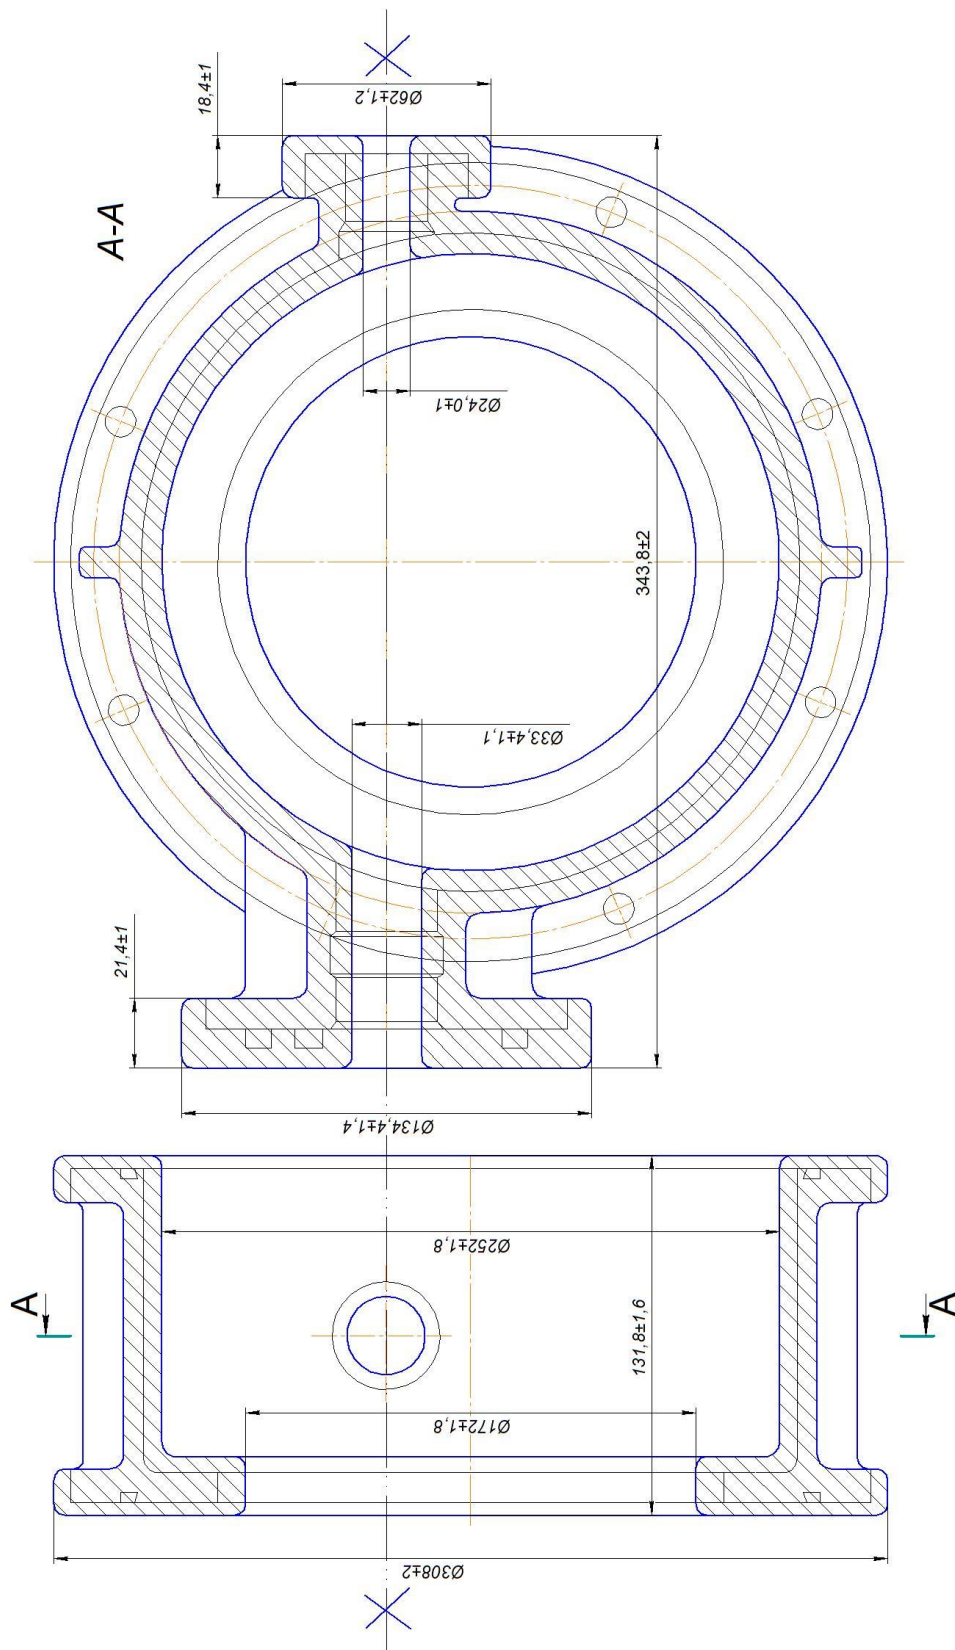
Ескіз заготовки корпусу для литва в земляній формі з машинним формуванням
